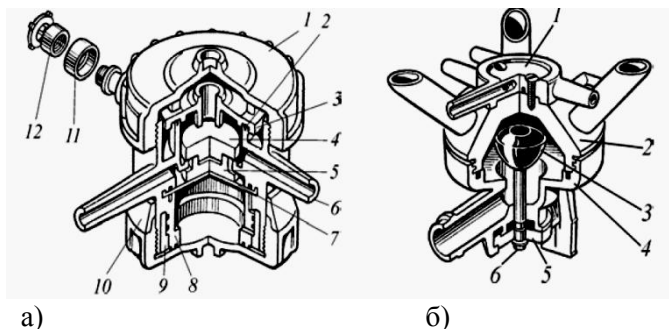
Пульсатор доильного аппарата АДУ-1. а: 1 – гайка; 2 – прокладка; 3 – крышка; 4 – клапан; 5 – обойма; 7 – корпус; 8 – корпус камеры управления; 9, 10 – уплотнительные кольца и коллектор; б: 1 – распределитель; 2 – корпус; 3 – резиновый клапан; 4 – крышка; 5 – резиновая шайба.
